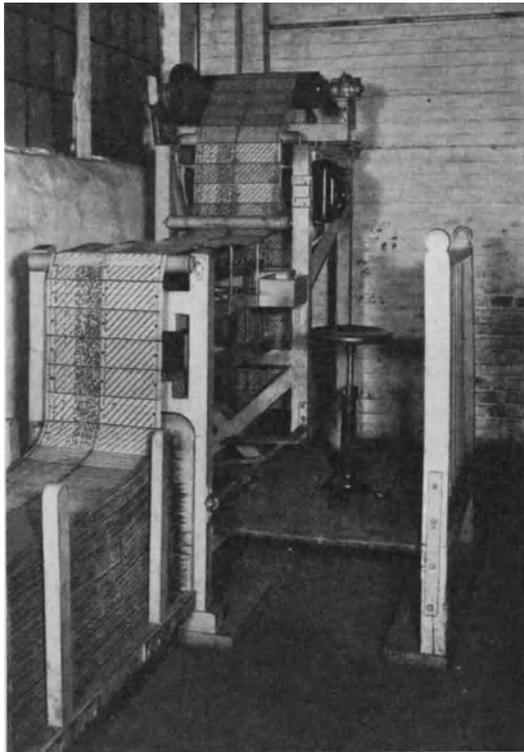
Ansicht einer Karten-Reparatur-Maschine.
